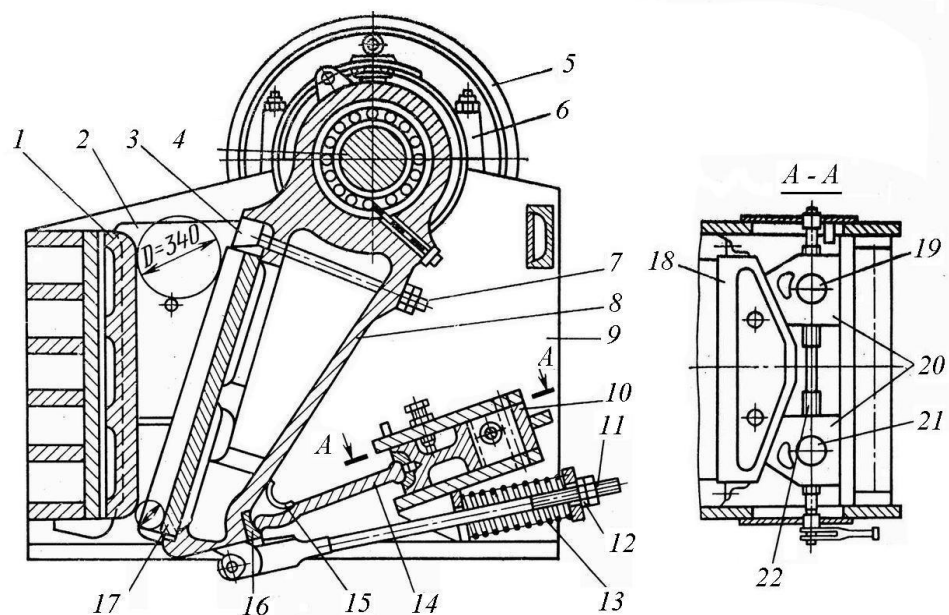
Конструкція щоккової дробарки з складним рухом щоки
